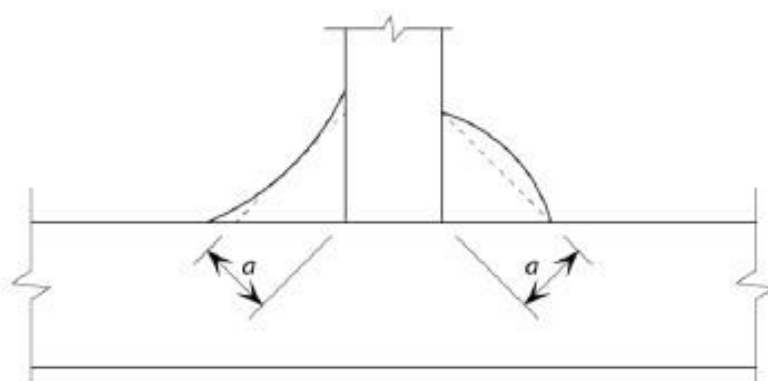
Espesor de garganta de una soldadura. (2)
